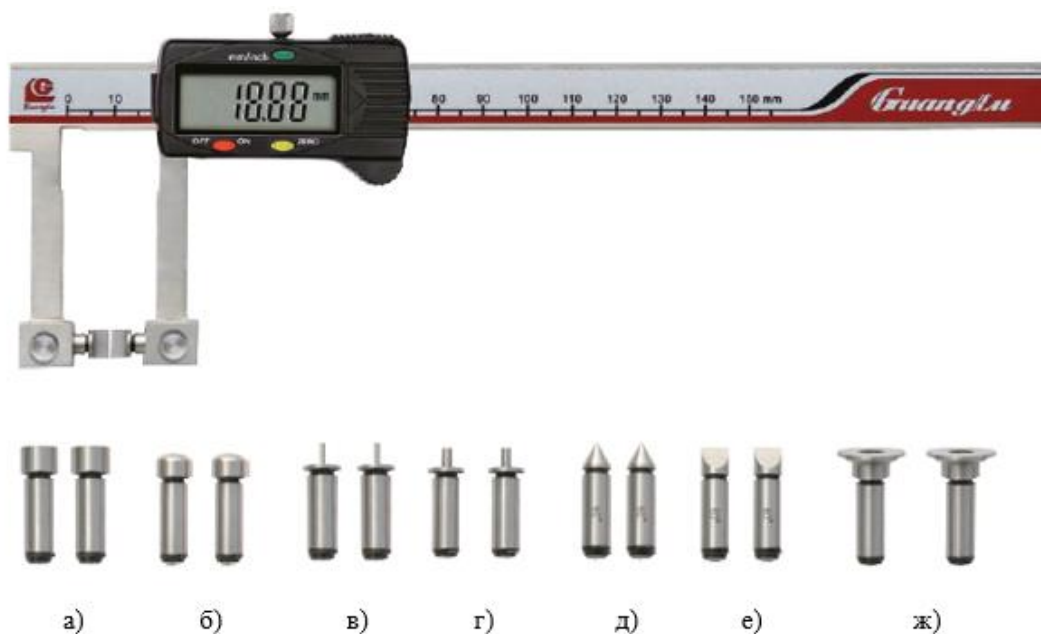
Общий вид штангенциркулей модификации 115, исполнений 441А, 442А, 443А, 445Z-А и комплекты сменных измерительных вставок; а) – цилиндрические с плоскими измерительными поверхностями; б) – цилиндрические со сферическими измерительными поверхностями; в) – с плоскими измерительными поверхностями; г) – цилиндрические с точечными измерительными поверхностями; д) – с коническими измерительными поверхностями; е) – с призматическими измерительными поверхностями; ж) – тарельчатые с плоскими измерительными поверхностями
